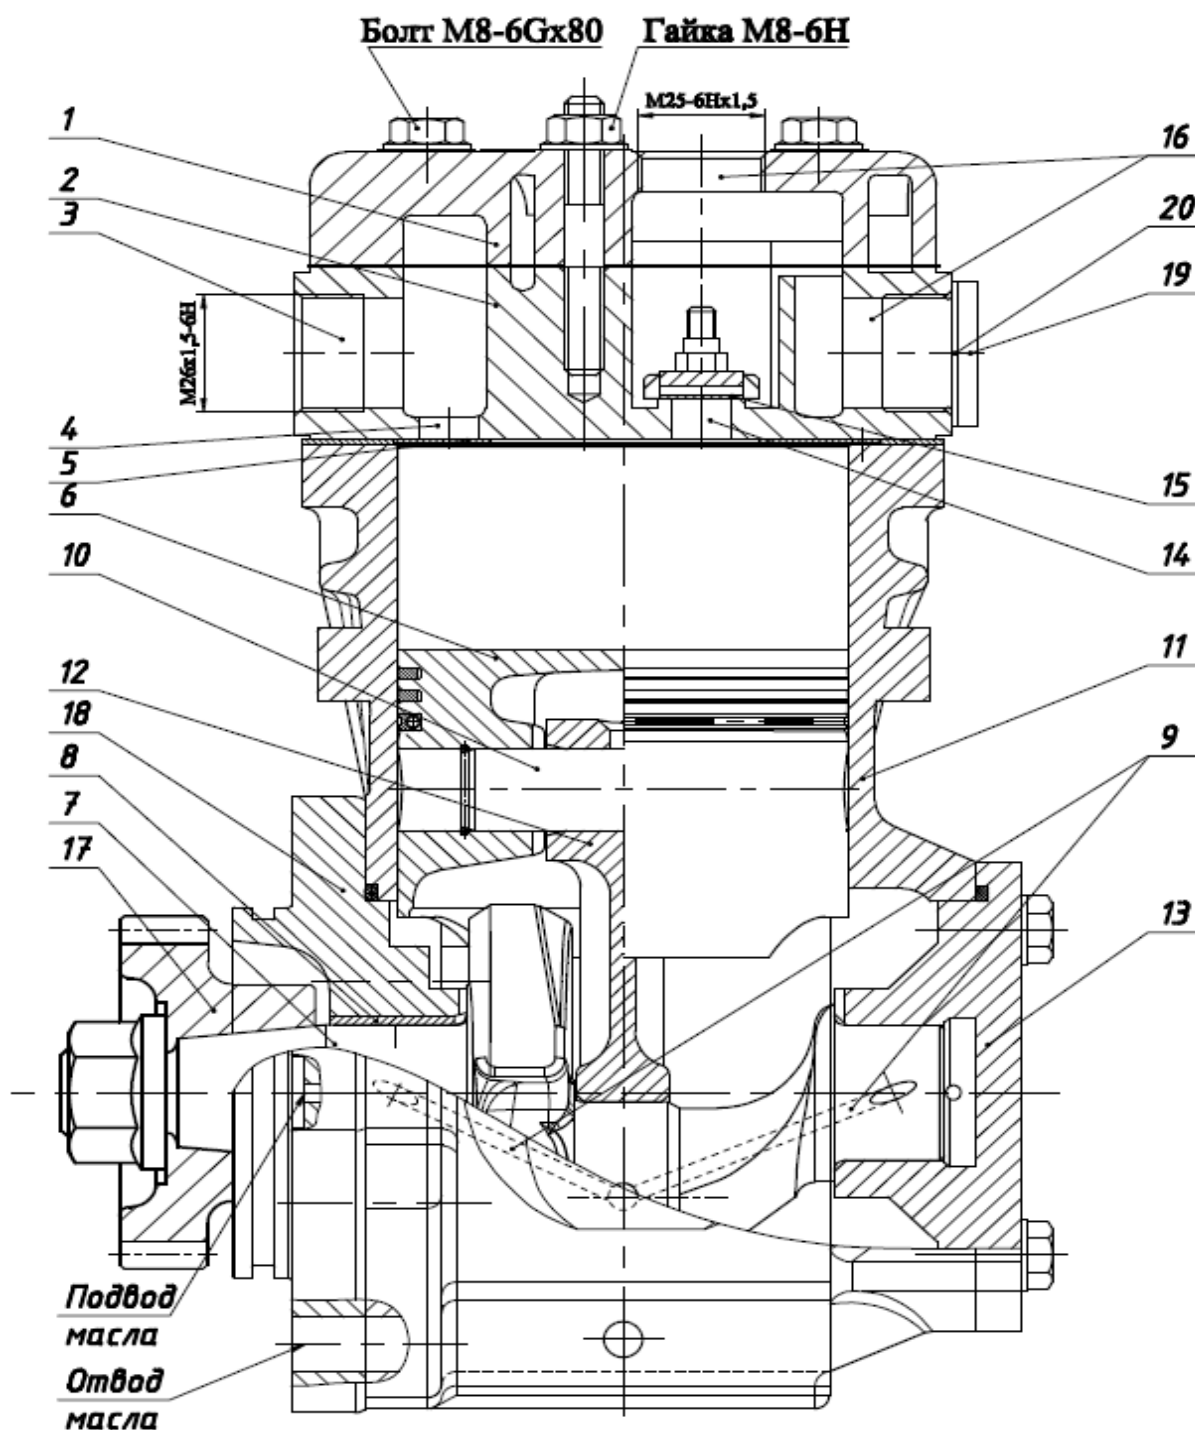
г. Принципиальная схема компрессора АМ.3509015-12:
